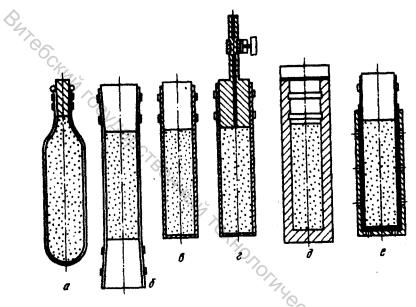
Пресс-инструмент для гидростатического прессования:
